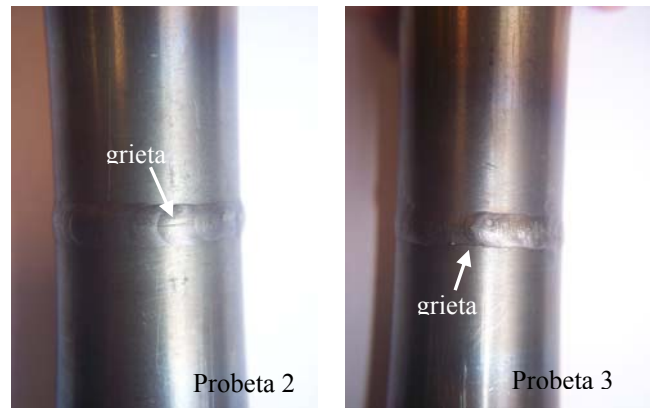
Aspecto de las probetas 2 y 3 tras el ensayo. Se puede observar que la grieta en la probeta 2 recorre la zona fundida del cordón de soldadura, mientras que en la probeta 3, se localiza en la zona afectada por el calor inferior adyacente a la soldadura.
